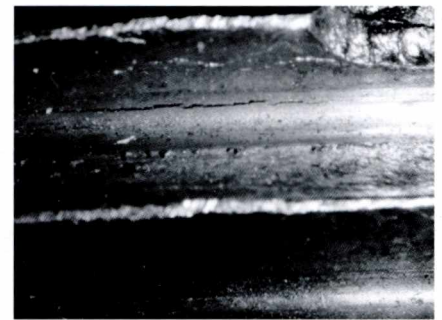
Fisura en la base del filete siguiente a la Fractura I.
